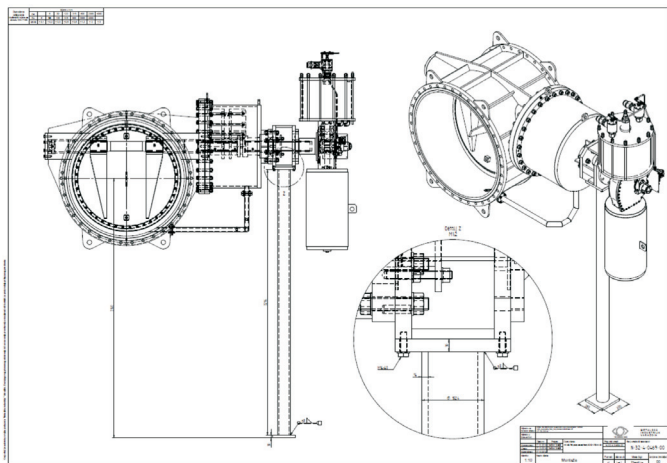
Обратный клапан MIV с опорой для пневмопривода ROTORK
